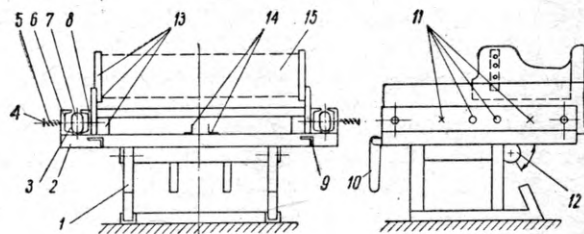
Пневматическая вайма для сборки корпуса пианино: 1 — станина-основание; 2 — поворотная подъемная рама; 3 — зажимное устройство; 4 — направляющий шток; 5 — спиральная пружина; 6 — неподвижная траверса; 7 — пневмокамера; 8 — подвижная траверса; 9 — регуляторы уровня боковых стенок; 10 — рычаг подъема; 11 — механизм управления ваймой (два распределительных пневмокрана, манометр, редуктор сжатого воздуха); 12 — ось поворота; 13 — узлы склейки; 14 — направляющие; 15 — место установки шульрамы
